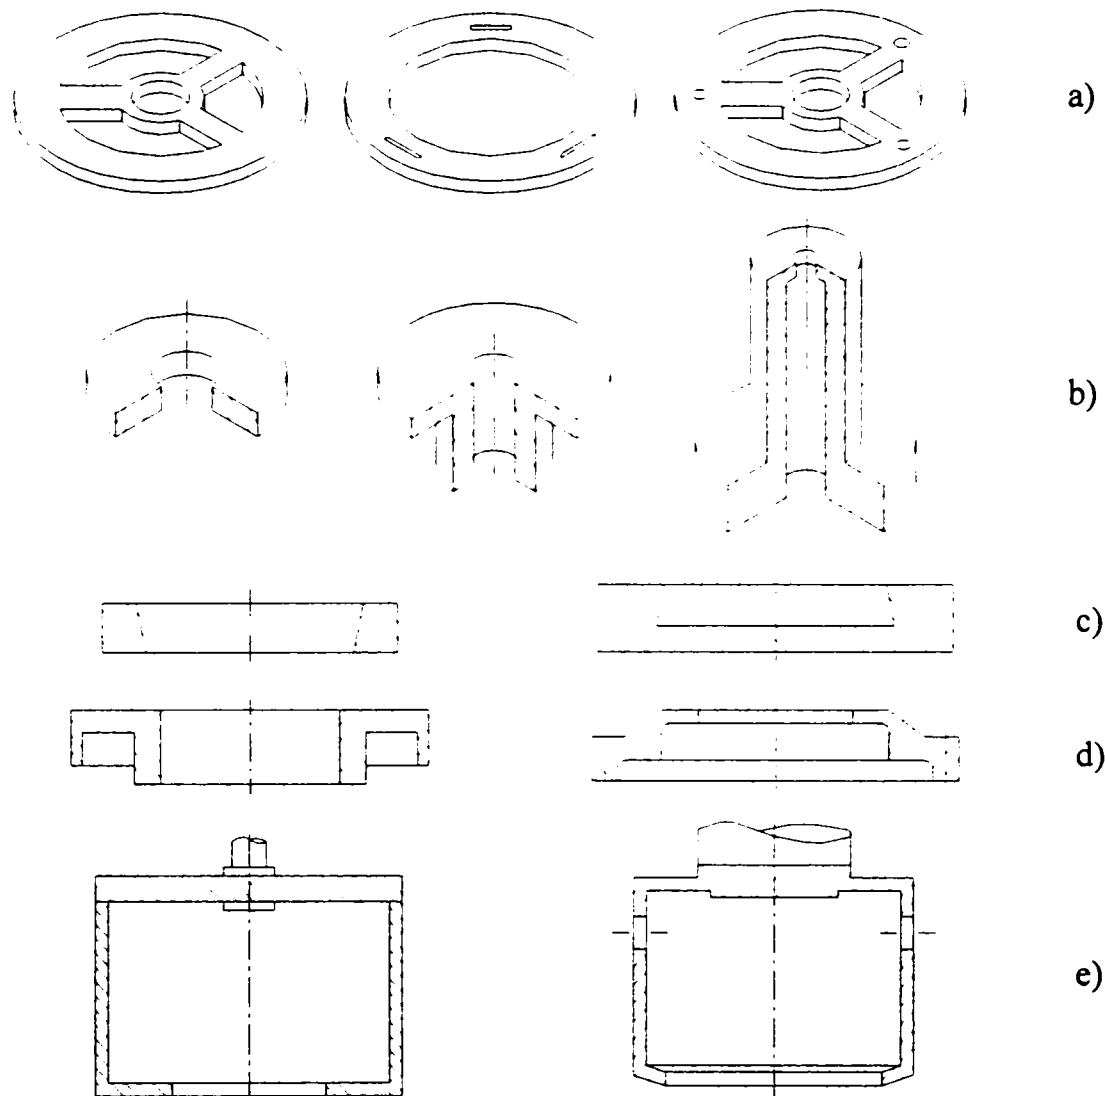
Elemente rigide din structura dispozitivelor de complianță
